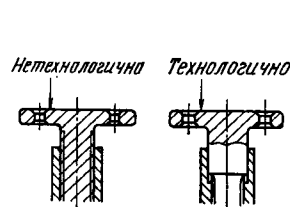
Резьбовые соединения с опорными поясками.
